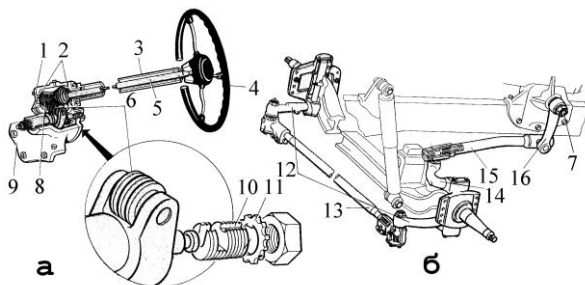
Рулевой механизм (а) и рулевой привод (б): 1 – нижняя крышка; 2 – конические подшипники; 3 – рулевая колонка; 4 – рулевое колесо; 5 – рулевой вал; 6 – ролик; 7 – вал сошки; 8 – червяк; 9 – корпус; 10 – регулировочный винт; 11 – шайба; 12 – рычаги поворотных цапф; 13 – поперечная тяга; 14 – верхний поворотный рычаг; 15 – продольная тяга; 16 – рулевая сошка
